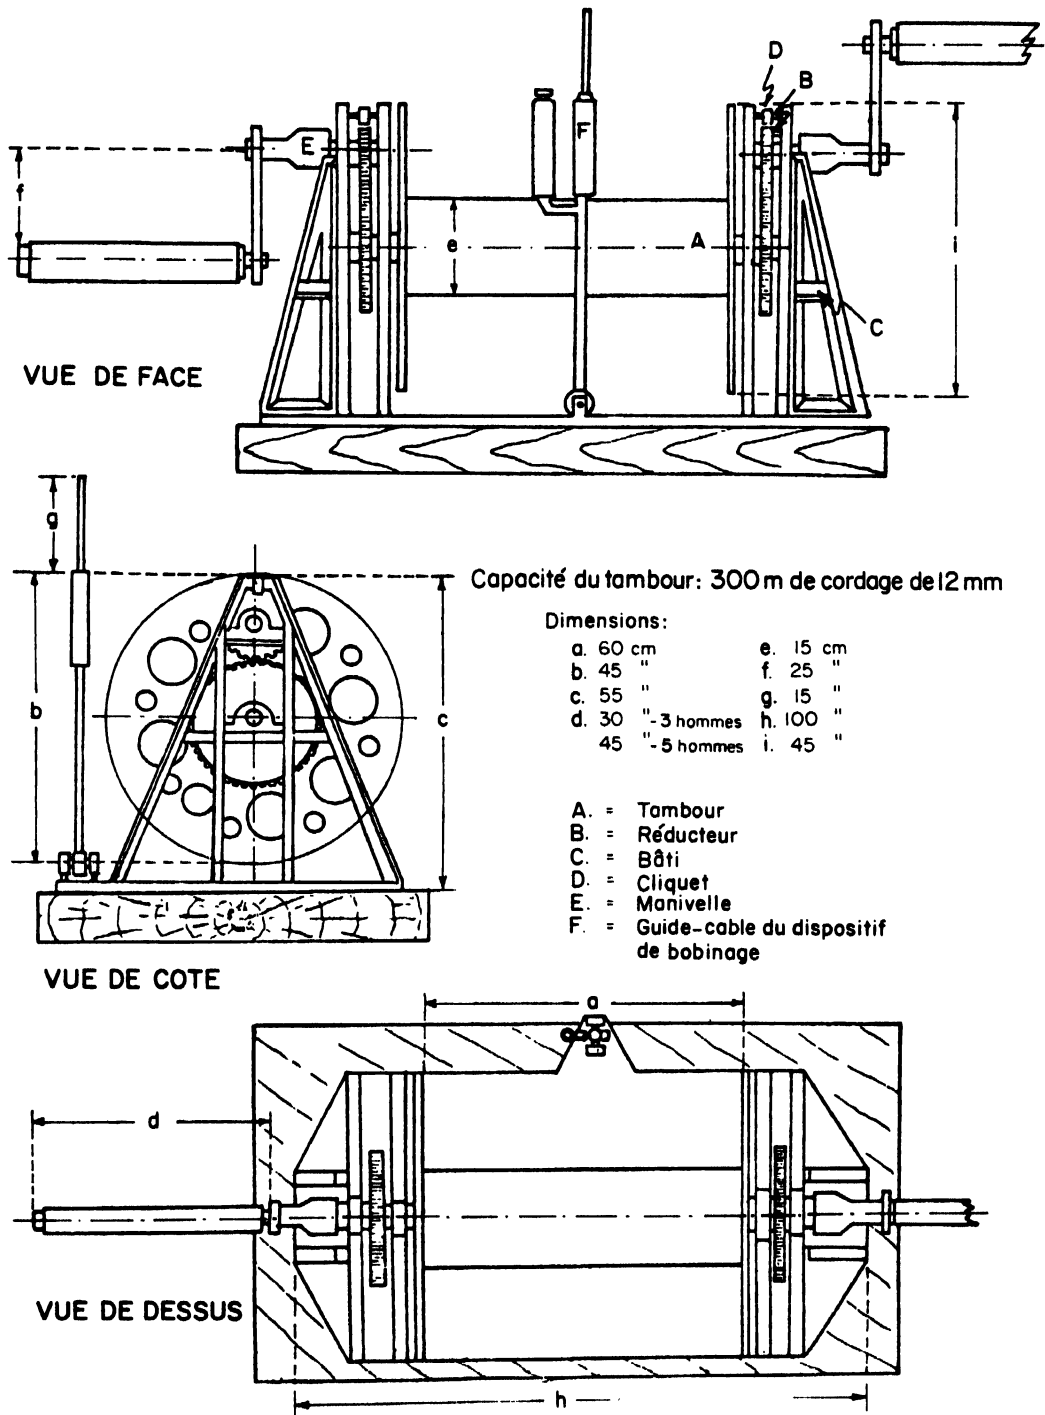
DETAILS DE CONSTRUCTION D'UN TREUIL A MAIN
